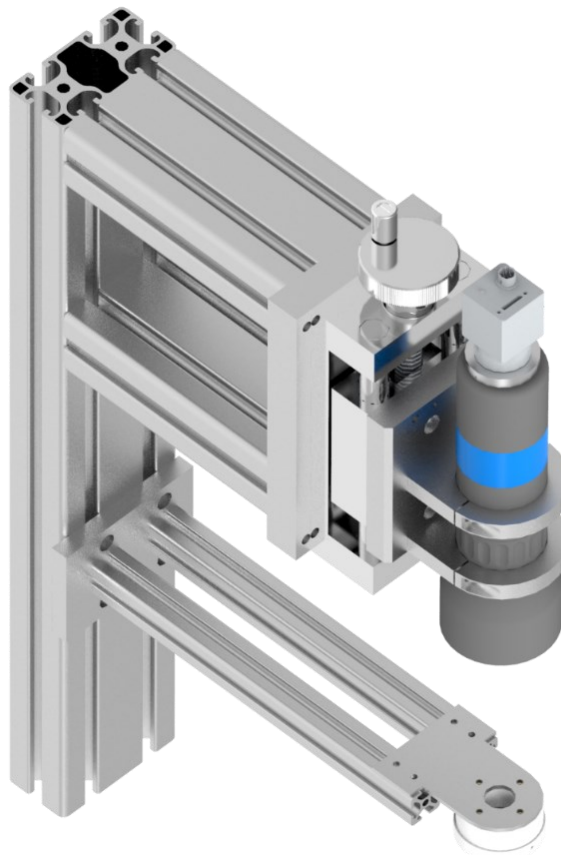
Rendering struttura supporto sistema di visione verticale
